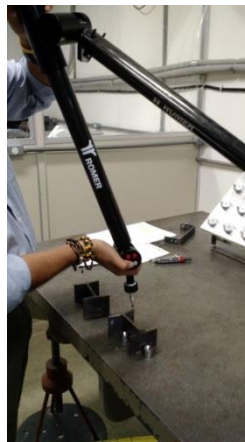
Amostras da viga Perfil-I Viga V1 e V2.
